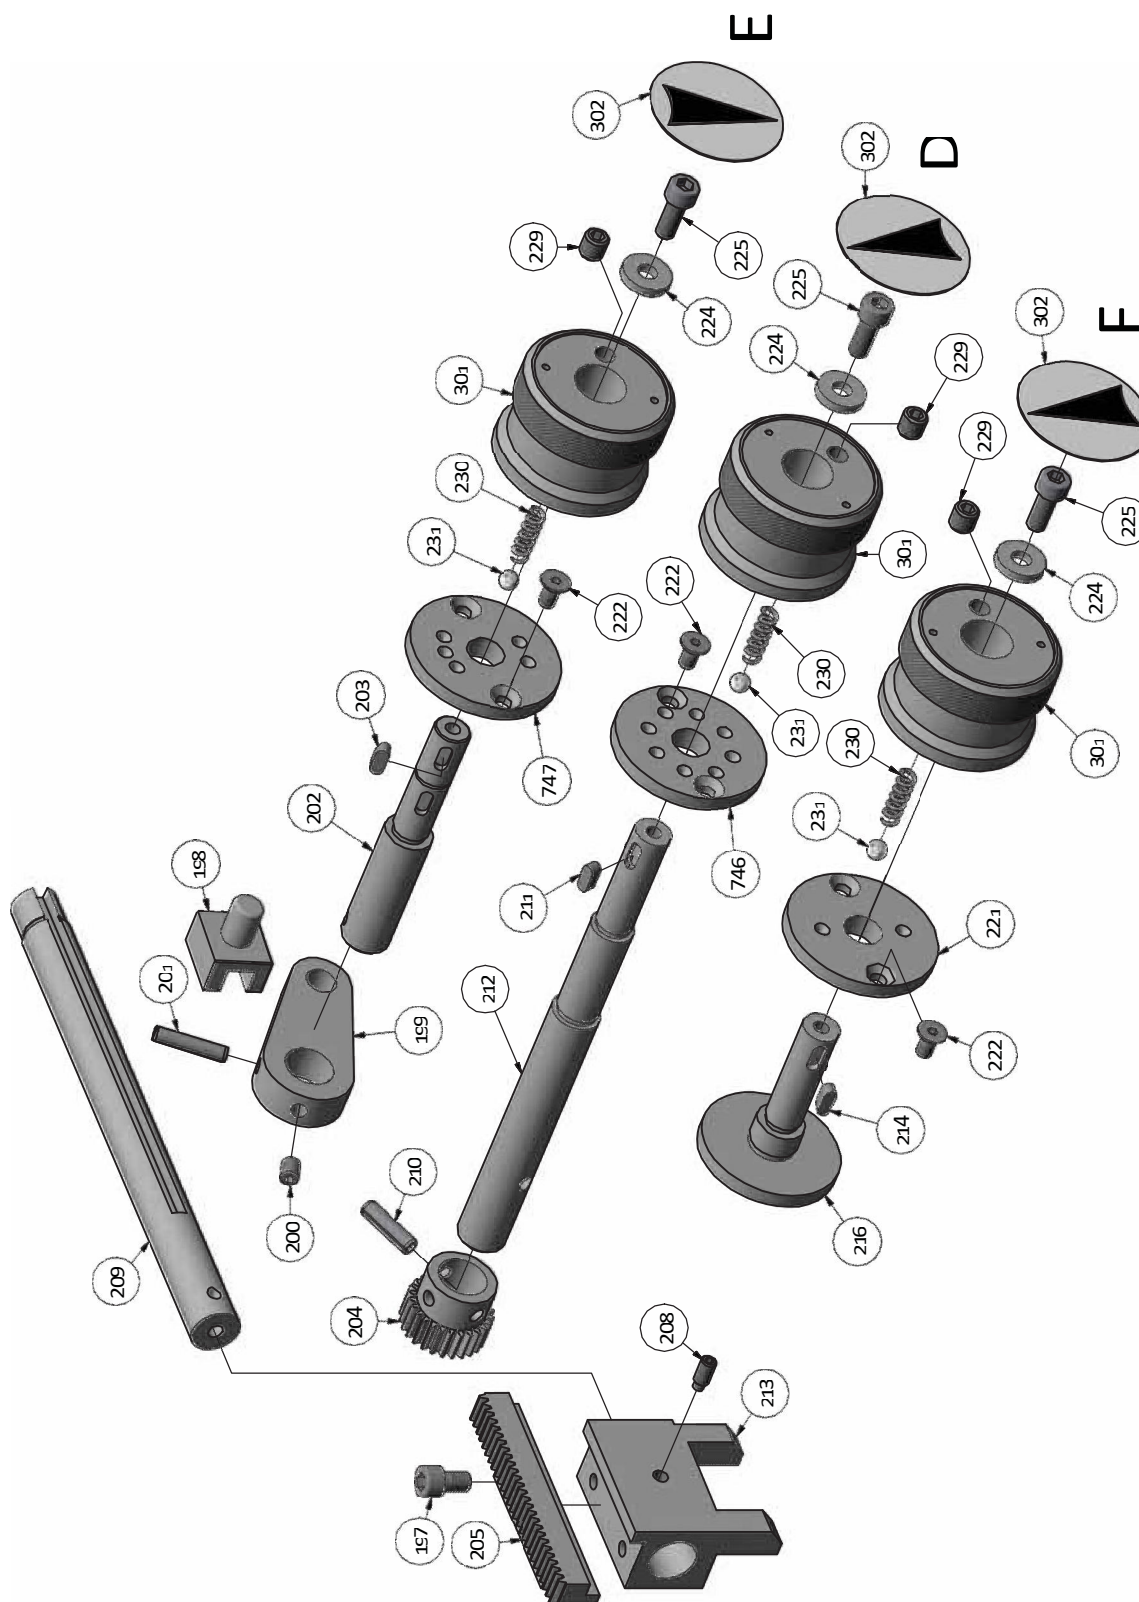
Vorschubgetriebe –Engranaje de avance
